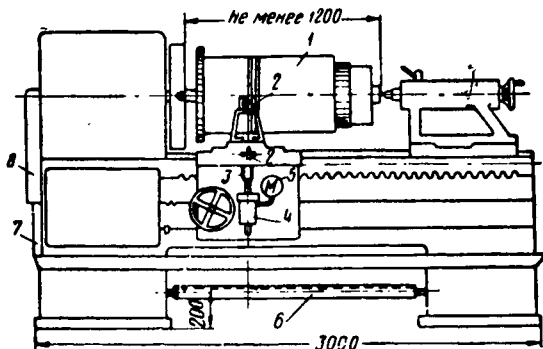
Общий вид токарного станка, приспособленного для бандажировки якорей:
